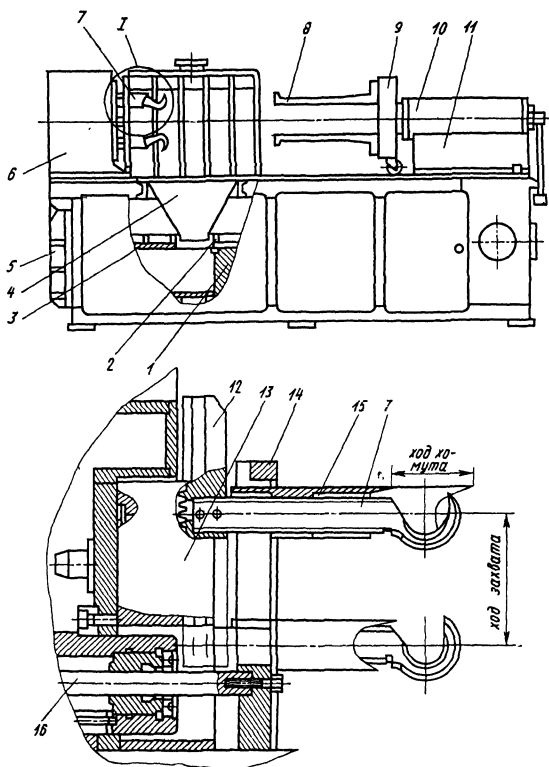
Станок типа УПО-1 для удаления обмотки из статоров
